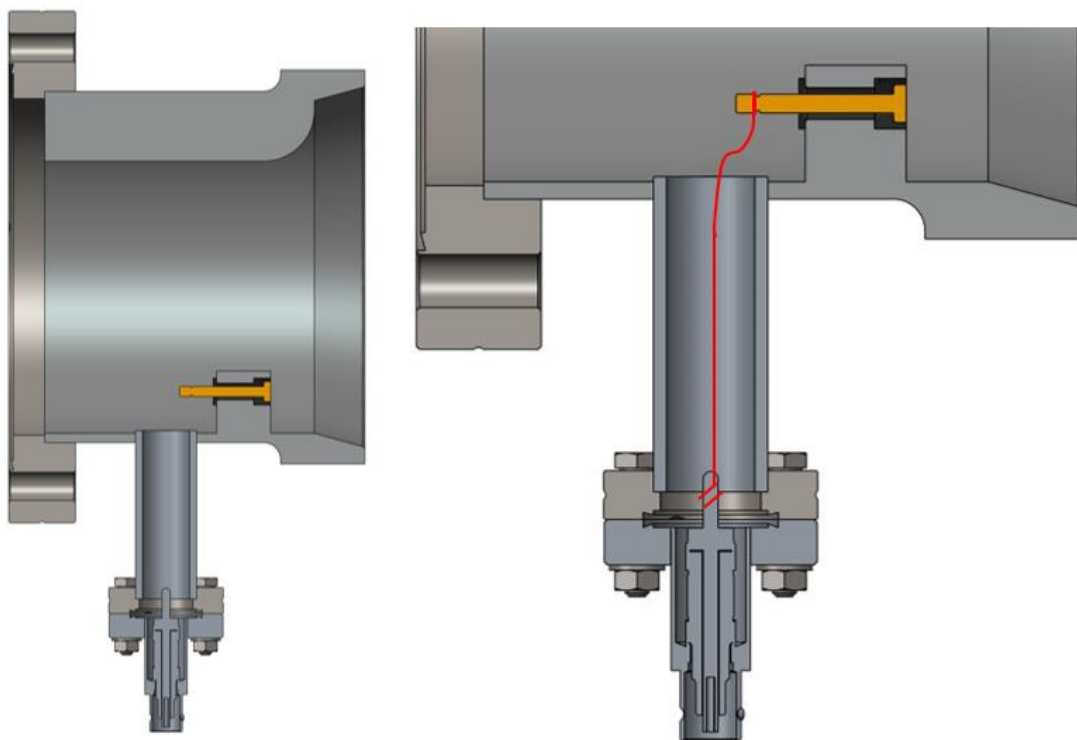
Vista in sezione e la rappresentazione del collegamento elettrico
